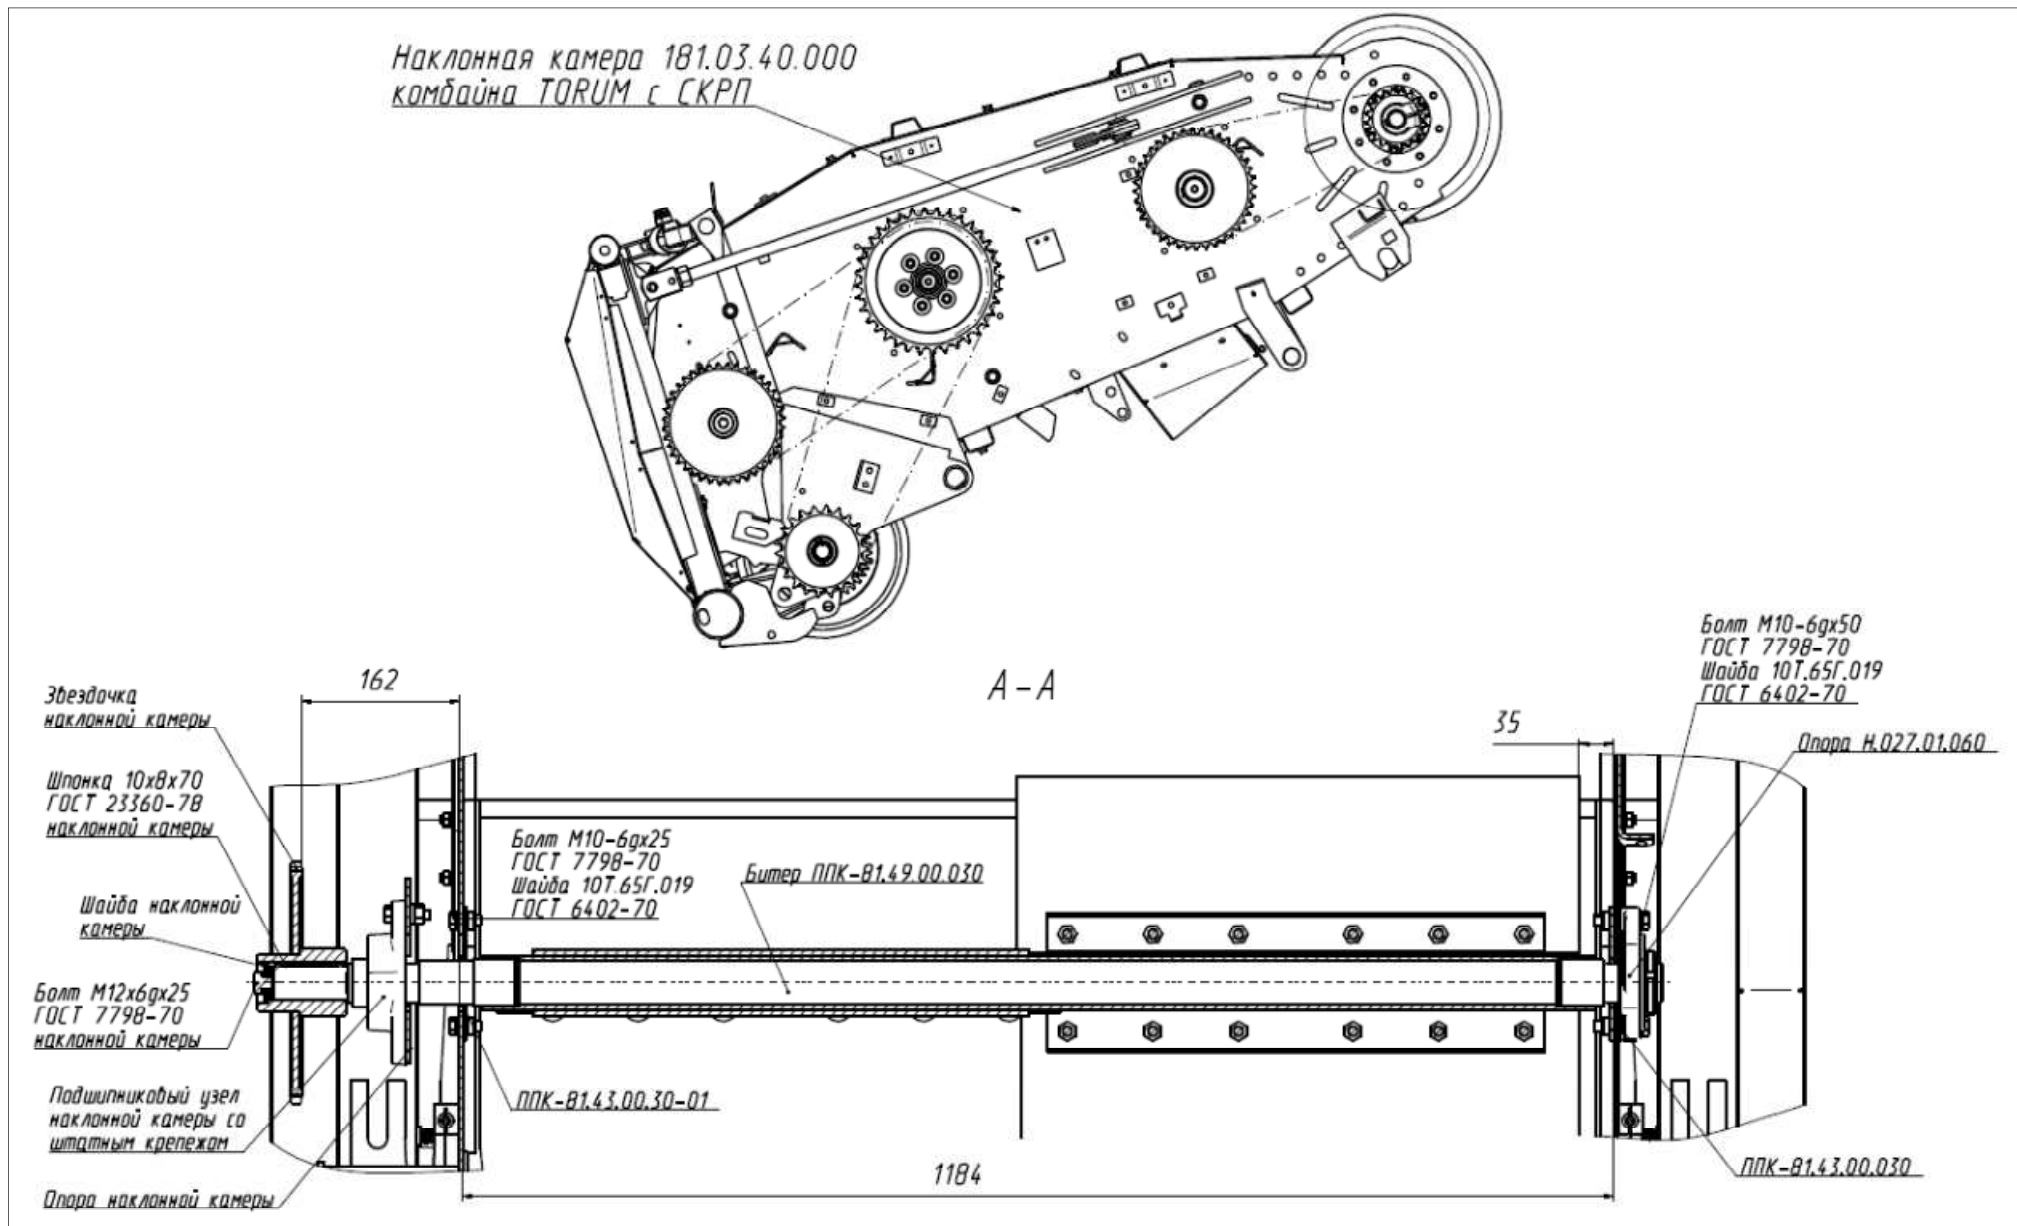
Установка битера для модели ППК-675-49 и ППК-875-49
